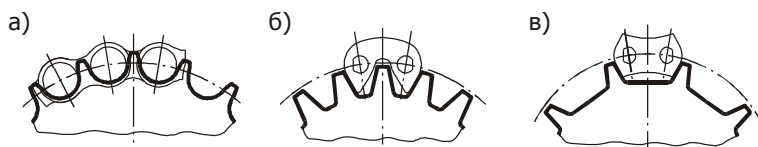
Зацепление звездочки с цепью: а – роликовой;
